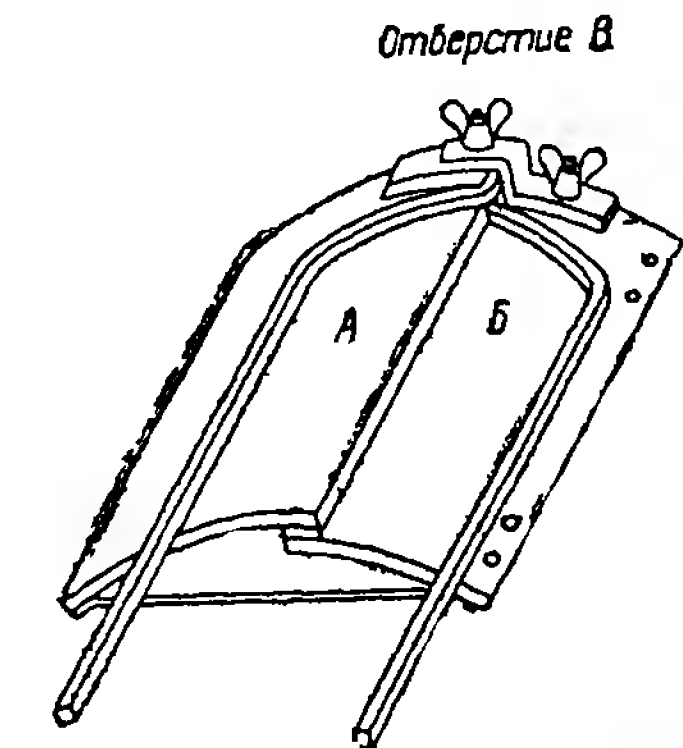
Приспособление для выгиба лобовой части по радиусу.
